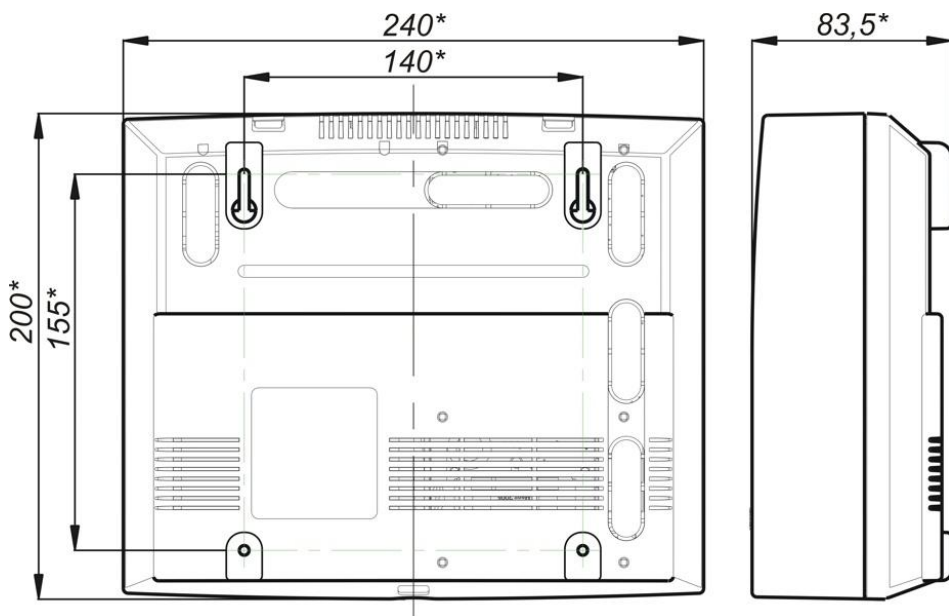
Габаритные и установочные размеры приборов ВС-ПК2(4,8).
